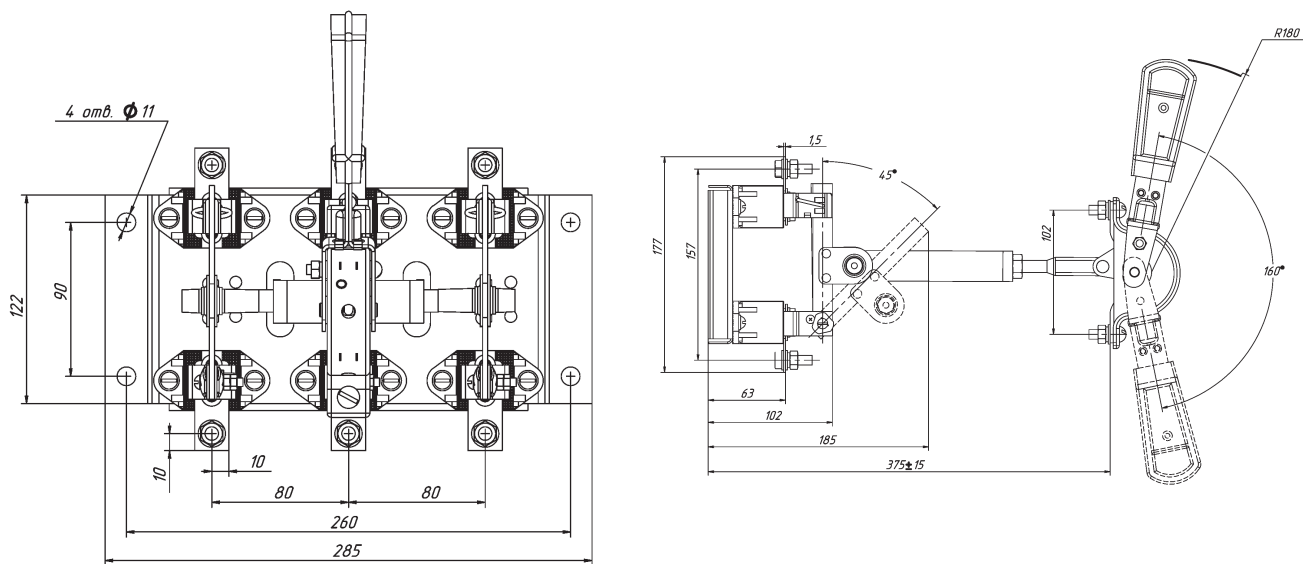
Разъединитель серии Р с центральным приводом РЦ-1, на номинальный ток 100 А.
